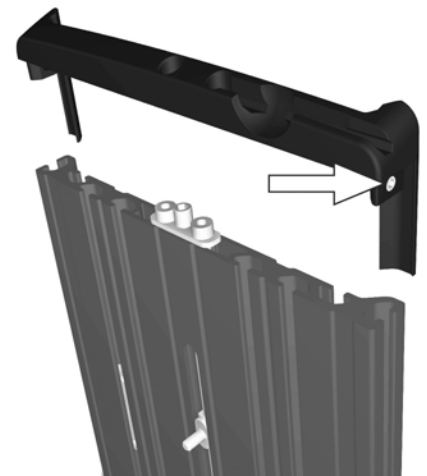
Die Endabdeckung des Rückenlehnenprofils ist mit einer Schraube auf der linken und einer Schraube auf der rechten Seite gesichert.
